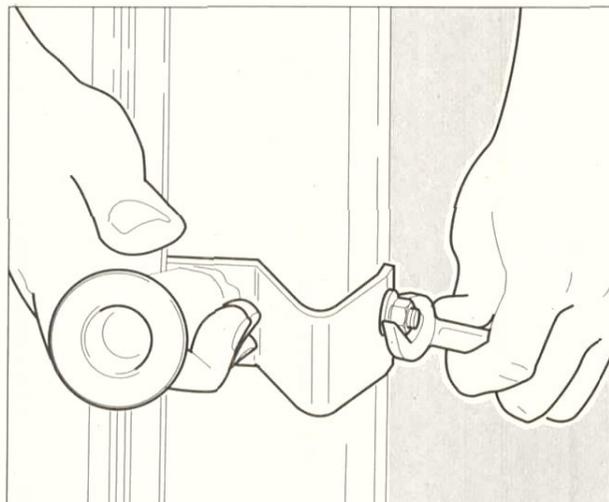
Tragegriffe liefern wir auf Wunsch. An beiden Seiten des Kollektors mit Befestigungsklemmen - höheren Absatz zum Kollektor - festschrauben. Sicheren Halt überprüfen!
